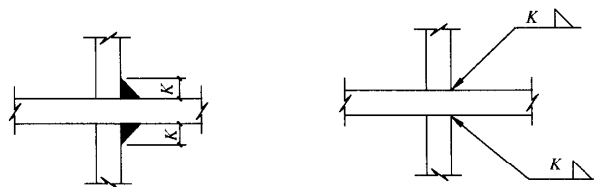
3 个及以上焊件的焊缝标注方法
